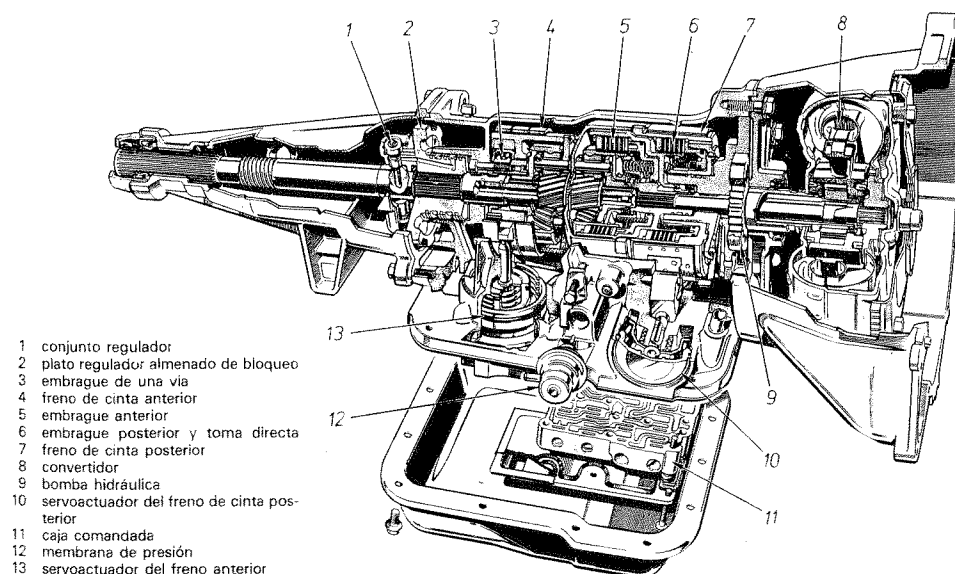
A Vista seccionada de una caja de cambios automática.
